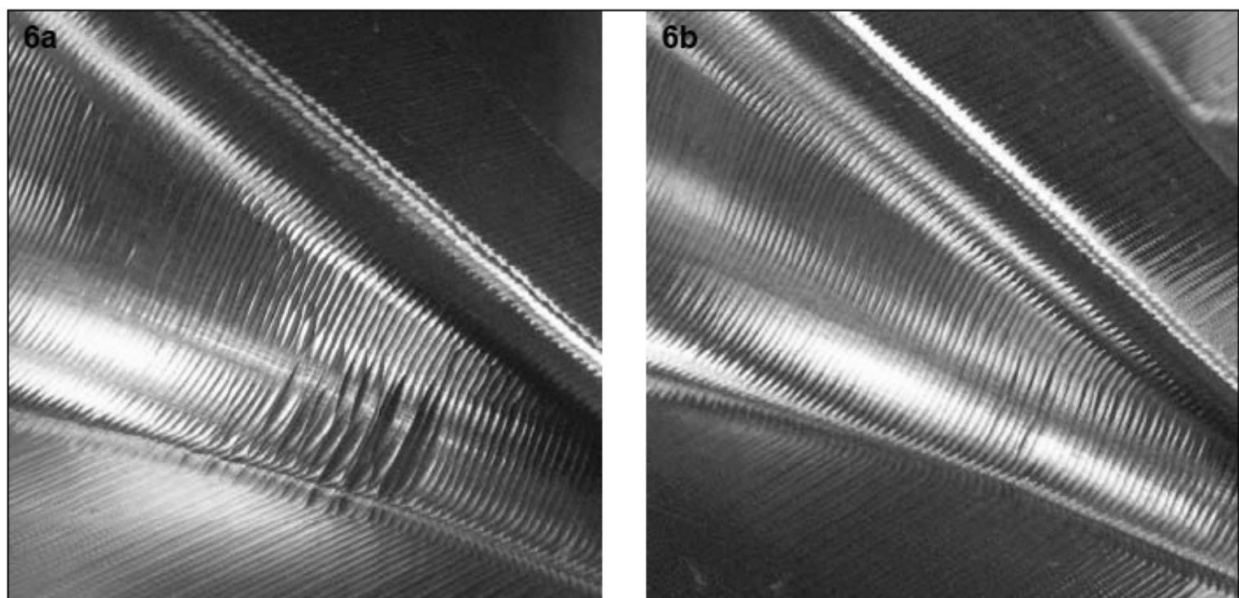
Процес рядкового фрезерування з реверсом: повторюваність сусідніх траєкторій фрезерування 6a: Відмінності між сусідніми траєкторіями призводять до поганої якості обробленої Поверхні 6b: Результат фрезерування за допомогою iTNC 530: рівномірна поверхня при прямих і реверсивних переміщеннях
